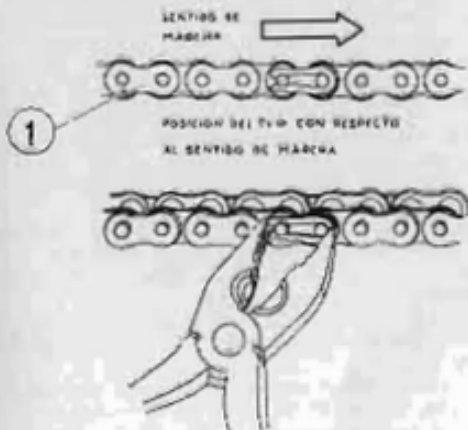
Cadena secundaria: Montaje y desmontaje del eslabón de unión.
